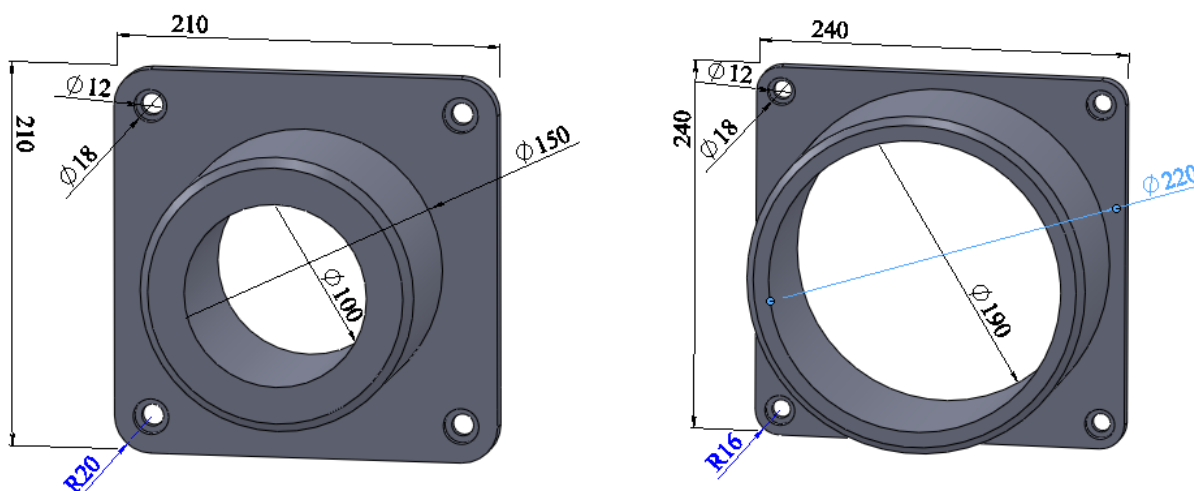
Конфигурации корпуса розетки соединителя `korpus_150` и `korpus_230`
